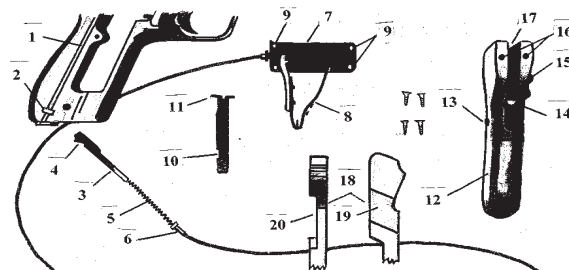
Конструкція пристрою «подвійне керування»: 1 — паз для повзуна; 2 — поперечний паз під втулку тросика; 3 — повзун; 4 — клиноподібний виступ; 5 — зворотна пружина повзуна; 6 — втулка тросика; 7 — верхня кришка; 8 — зворотна пружина тросика; 9 — отвори для шурупів; 10 — спусковий гачок (вид ззаду); 11 — вісь спускового гачка; 12 — руків'я (вид спереду); 13 — головка гвинта кріплення; 14 — перемикач; 15 — сосок перемикача; 16 — отвори для гвинтів передньої частини кришки; 17 — щілина для спускового гачка та зворотної пружини; 18 — верхня частина повзуна (збільшено, вид ззаду); 19 — виріз під спускову тягу; 20 — верхня частина повзуна (вид ззаду)
